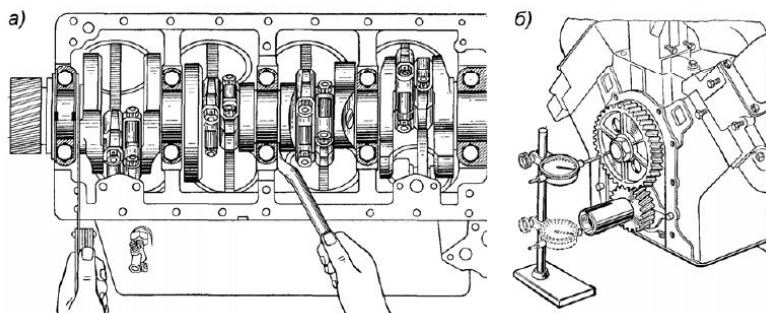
Контроль осевого зазора в упорном подшипнике коленчатого вала: а) - с помощью щупа; б) - индикаторным приспособлением.
